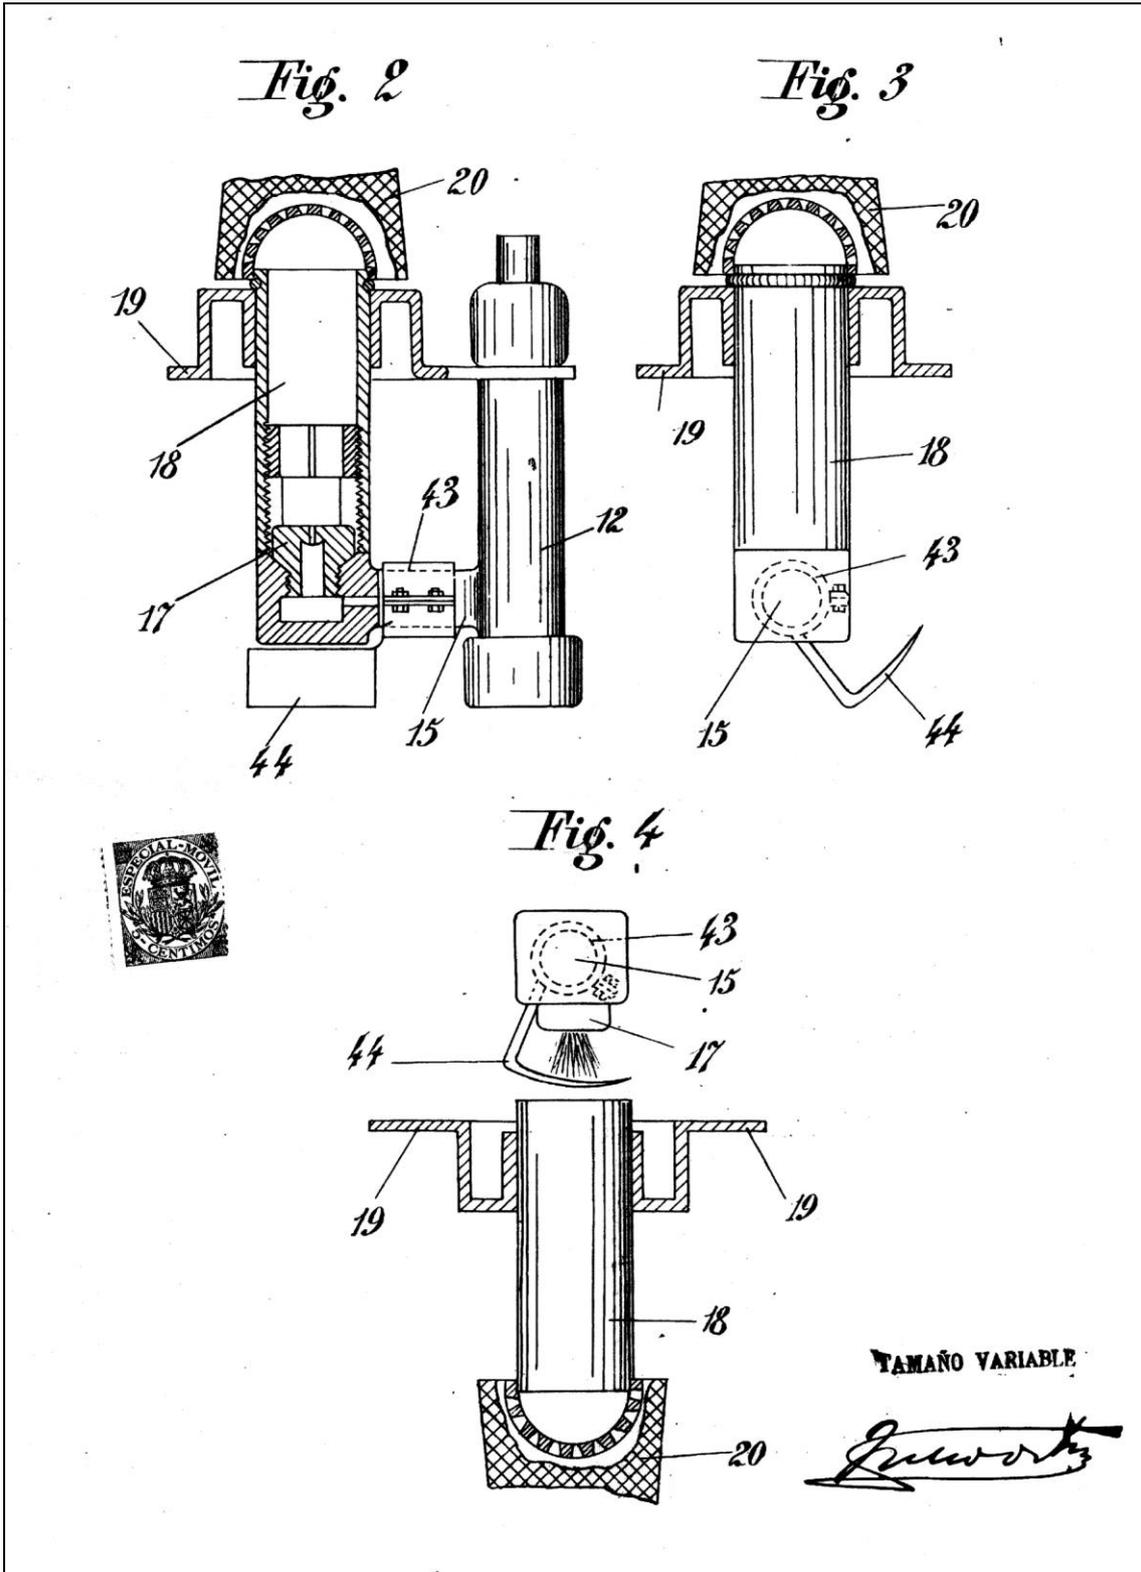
Detalle del cierre (Arch. J.M. Sanchis)
